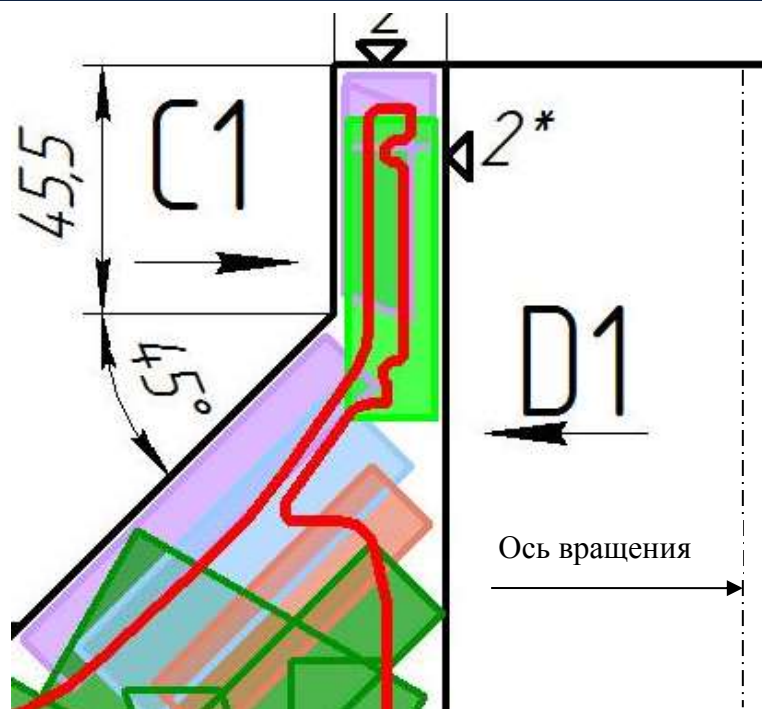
Сечение заготовки с наложенным контуром чистой детали (красная линия) и зонами контроля
